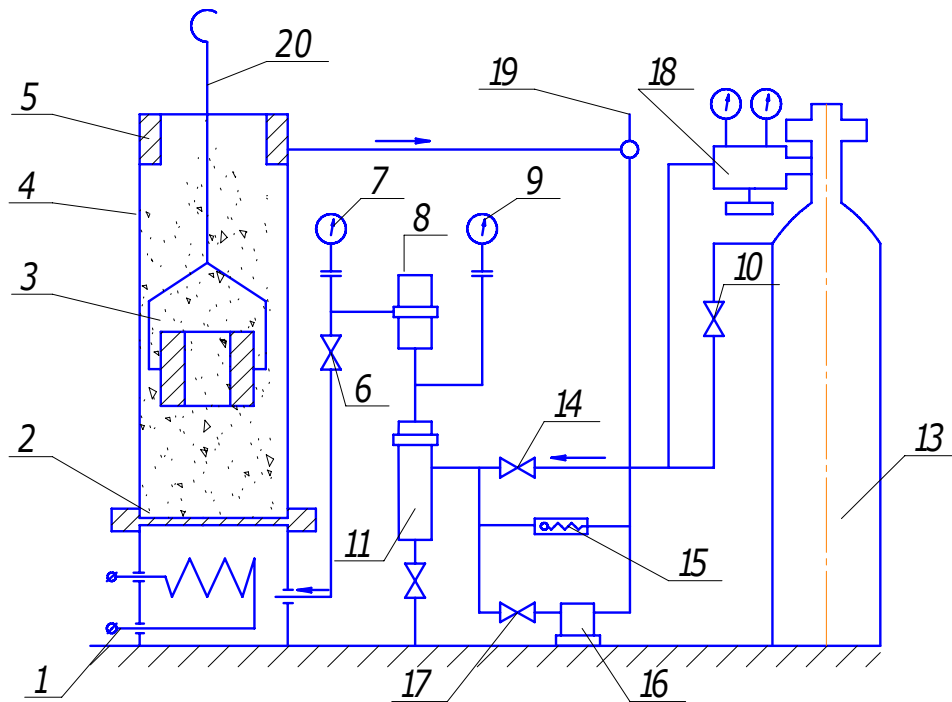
Установка для вихорового наплення полімерних матеріалів
